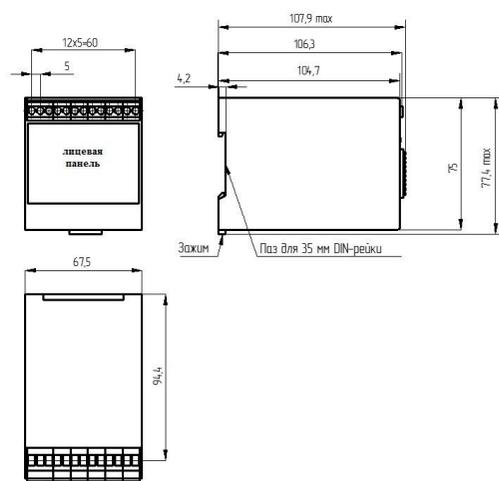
Общий вид, габаритные и установочные размеры реле
